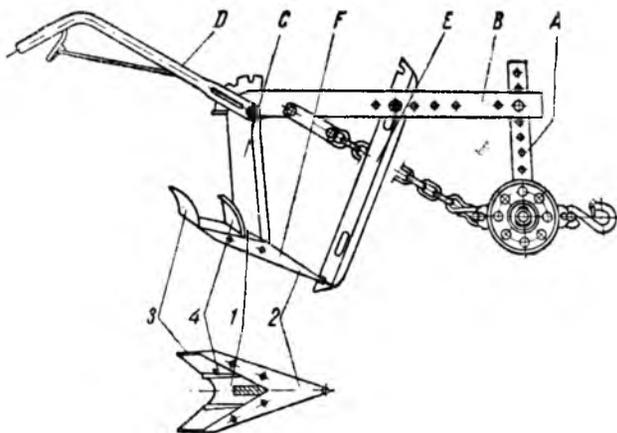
Схема лесного почвоуглубителя ЛЗ-56 с лапой конструкции Е. и Р. Рудницких: А — колесный передок; В — гредиль; С — стойка; Д — ручки; Е — черенковый нож; F — лапа; 1 — плита; 2 — лемех; 3 — поднимающиеся боковые ножевидные пластины; 4 — центральные поднимающие пластины.
